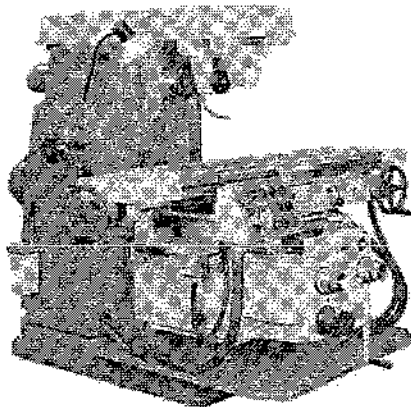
Горизонтально-фрезерный станок 6P83
